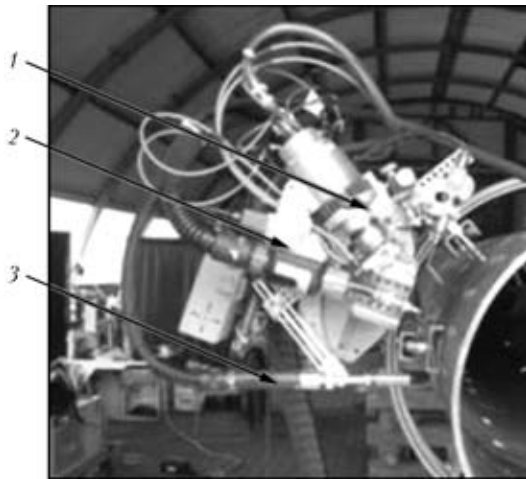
Сварочная головка с гибридной оснасткой для сварки корня и дуговая горелка для заполнения разделки: 1 — лазерная оптика; 2 — гибридная дуга; 3 — сварка МАГ верхнего слоя
